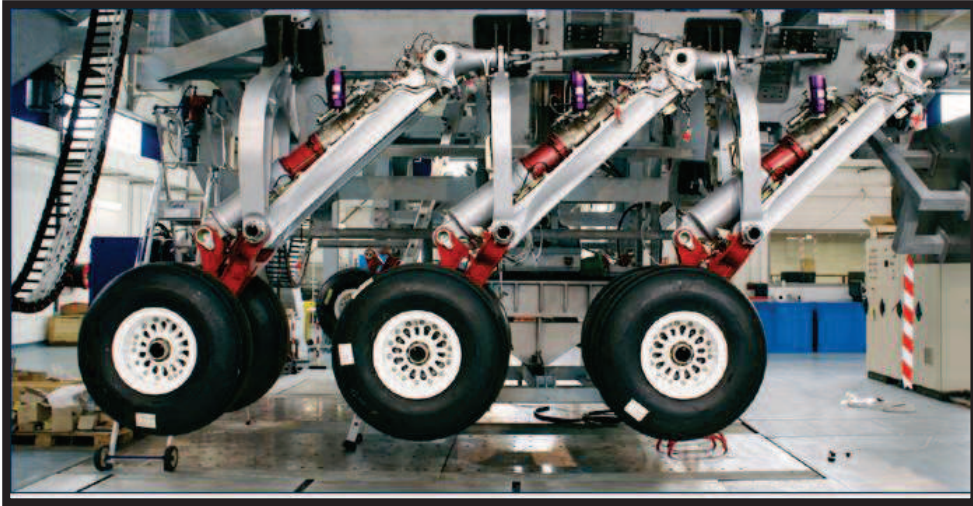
Tren de aterrizaje colocado en banco de prueba
